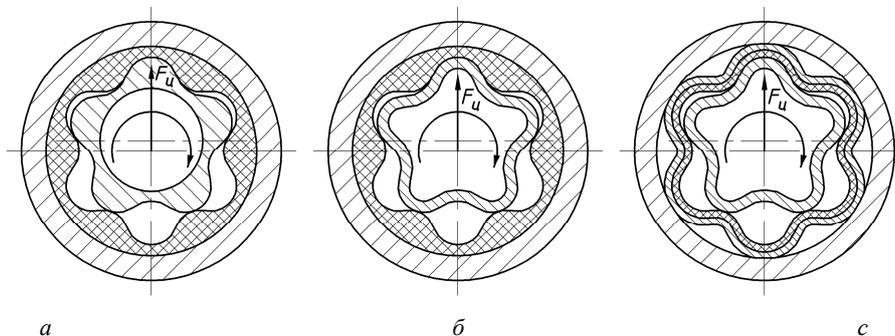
Торцовое сечение секций рабочих органов винтового забойного двигателя: а – стандартный статор с полым ротором; б – стандартный статор с облегченным ротором; в – армированный статор с облегченным ротором
